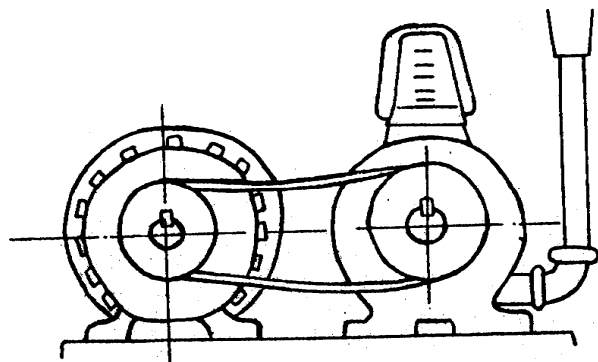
Несвоевременная регулировка натяжения ремней привода
